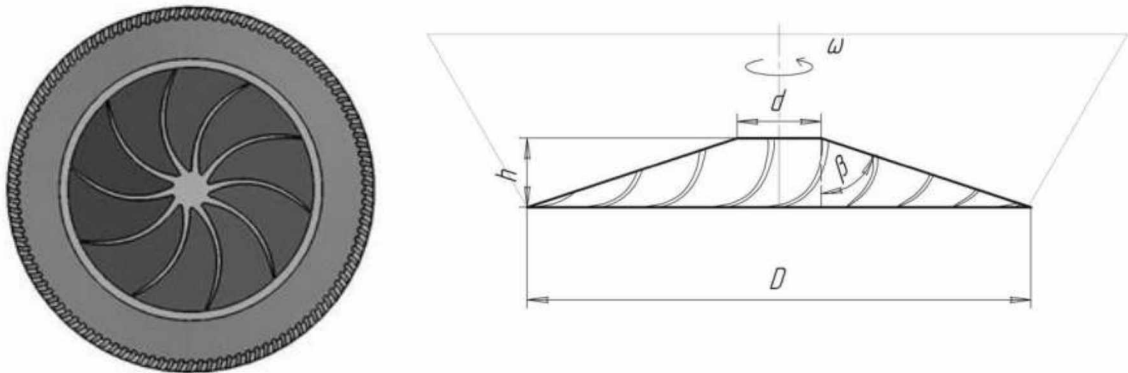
Загальний вид. Схема рухомого абразивного диска з криволінійними борозенками
